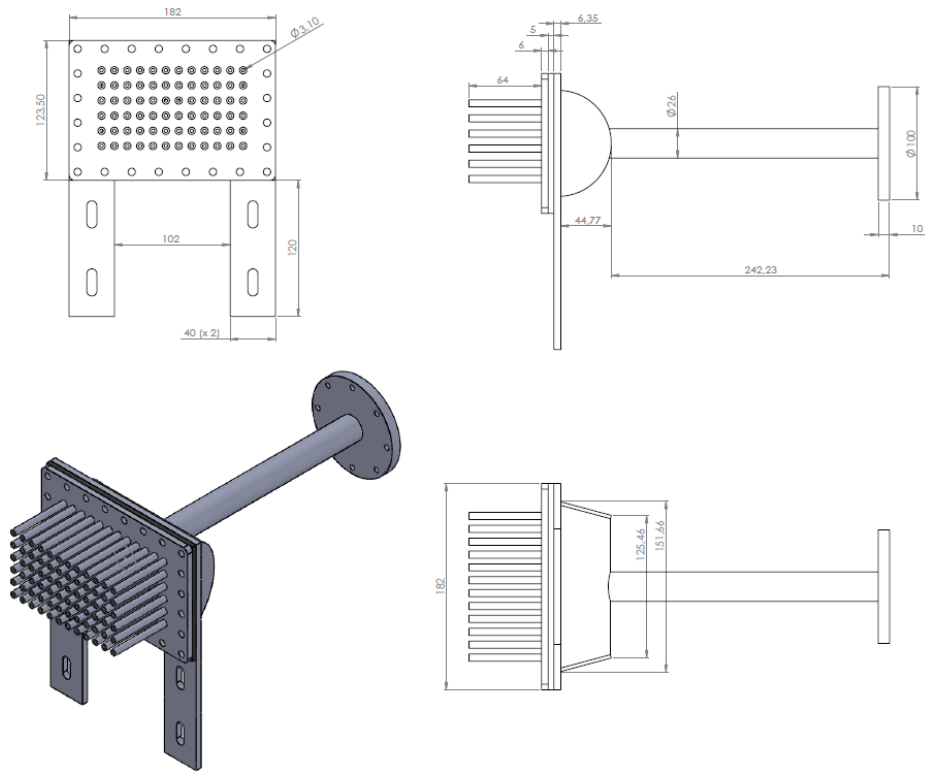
Desenho técnico da base metálica onde os canais de saída foram soldados.
